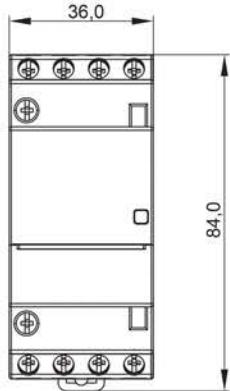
Габаритные размеры контакторов 100 А, 2Р / Figure 5 – Overall dimensions of 100 A, 2P contactors
